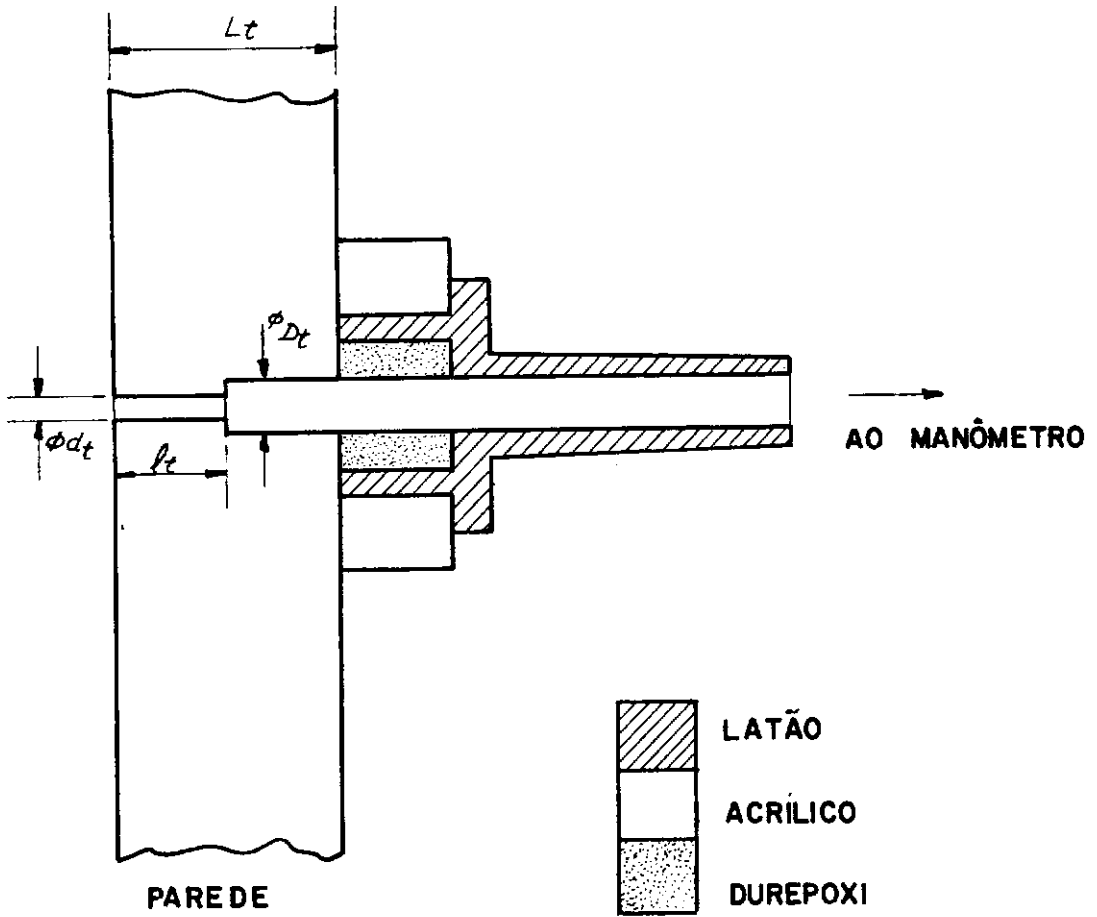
DIMENSÕES (INTERNAS) BÁSICAS DO DISPOSITIVO
